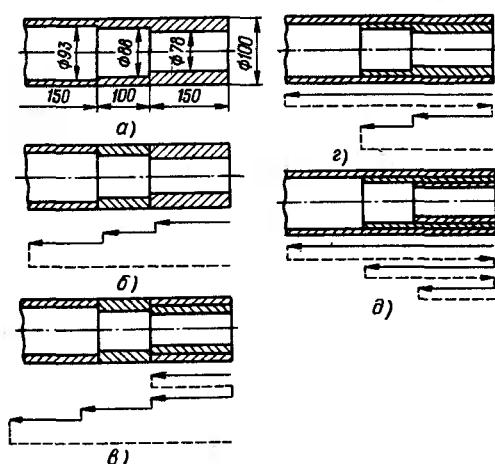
Схемы черновой обработки ступенчатых валов
